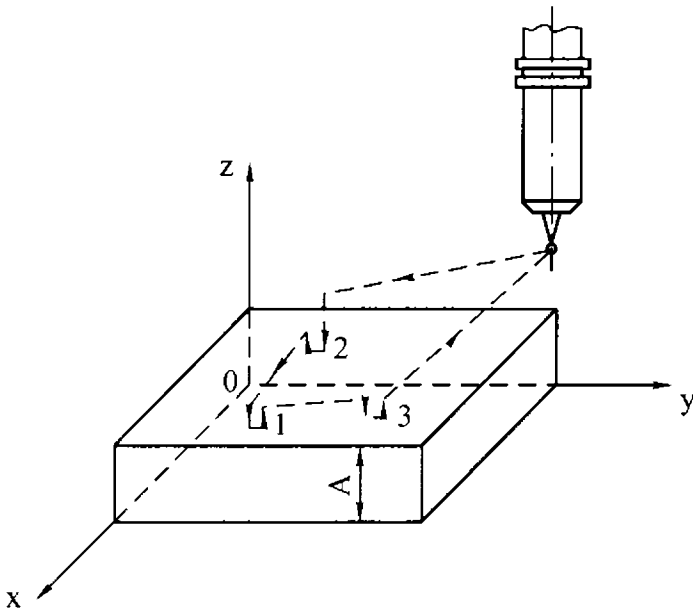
Схема вимірювання точності стану обробленої поверхні.
